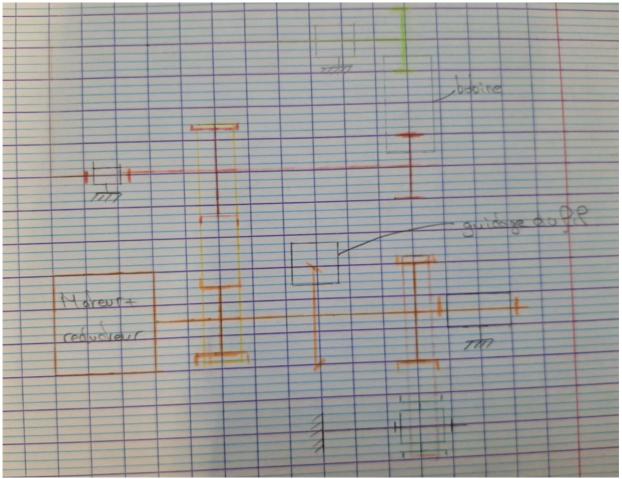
Schéma cinématique de l'ensemble, vue de dessus
